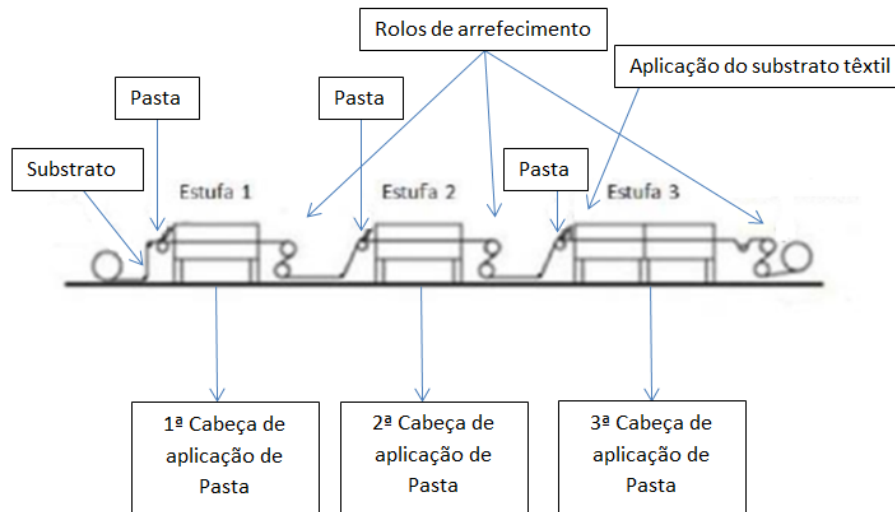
Representação da máquina de recobrimento da TMG Automotive, imagem adaptada de [47].
